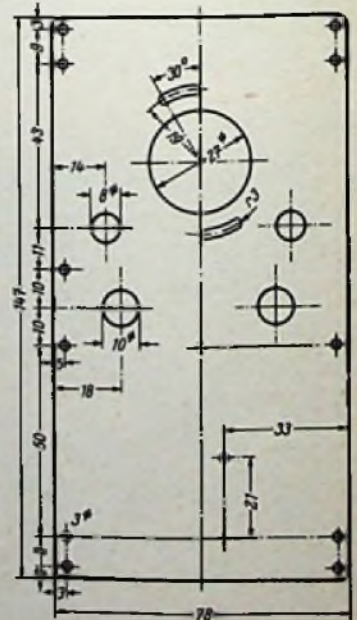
Chassisrückwand (Pos. 4). 1,5-mm-Aluminium; alle Bohrungen ohne Maßangabe 3 mm  $\varnothing$
